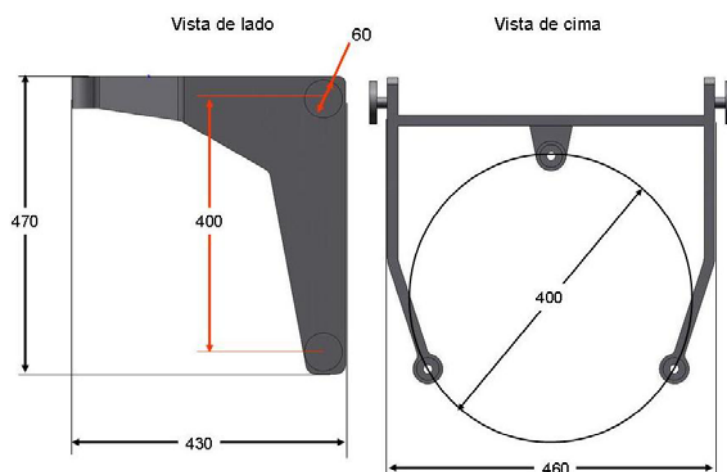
Cotas gerais da estrutura de suporte da câmara de vazamento.
